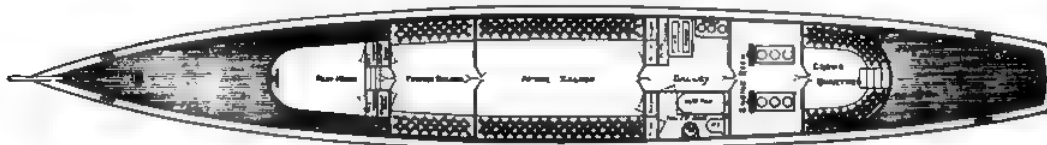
Grundriss zu obigem Kajüt-Segel-Boot. (Engine Room = Maschinenraum.)
